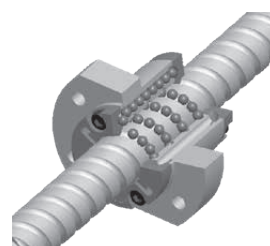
Kugelgewindemutter mit Kassetten-Rückführungssystem
